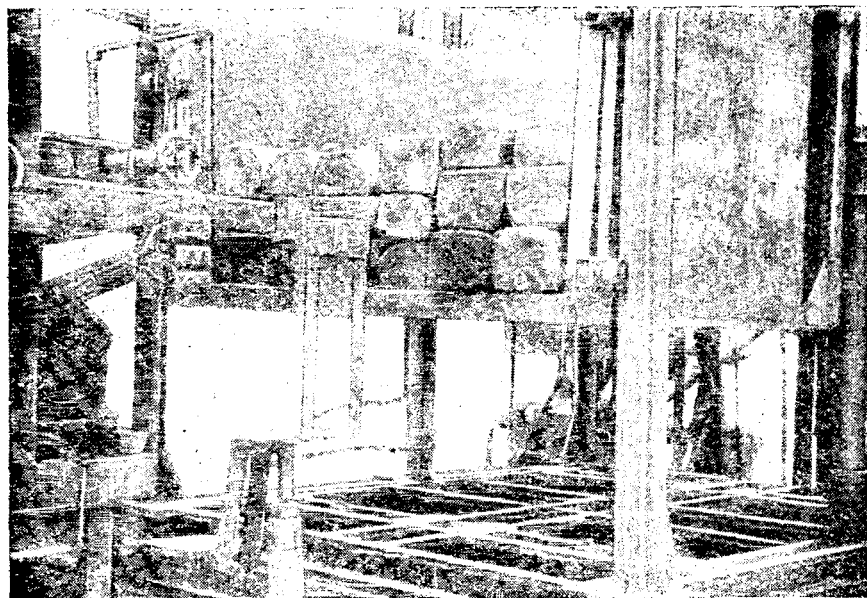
Бункер со шпалами, подготовленными для накальвания (верхний ряд шпал поднят на уровень стола станка)
